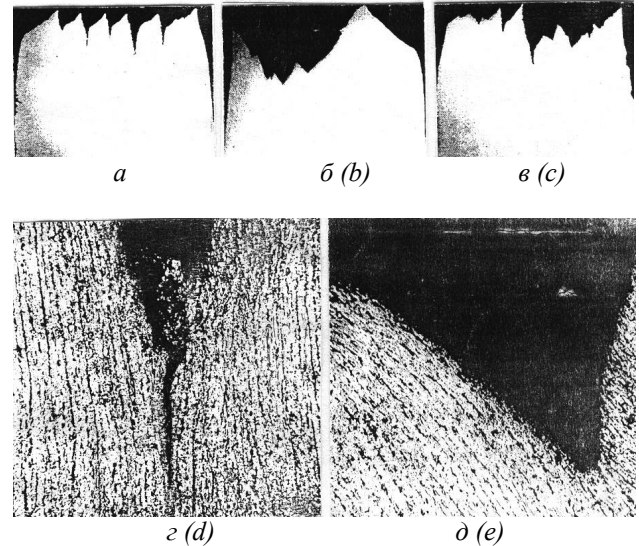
Поперечные сечения образцов ИППГ с расщеплениями в изломах : а – расщепления первого типа; б – расщепления второго типа; в – расщепления первого и второго типа; г – окончание расщепления первого типа; д – окончание расщепления второго типа / Fig. 2. Cross-section of DWTT specimens with laminations in fractures : a – the first type laminations; b – the second type laminations; c – laminations of the first and the second types; d – ending of the first type lamination; e – ending of the second type lamination
